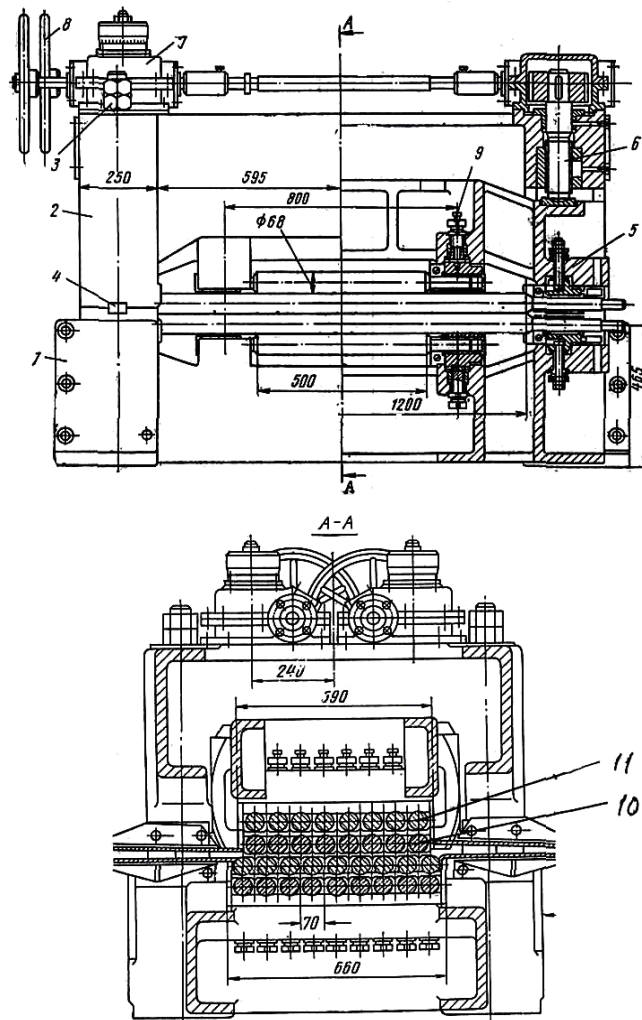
17 - роликова правильна машина з верхньою нахилу траверзою: 1, - станина нижня, 2 - станина верхня, 3 – болт, 4 - шпонка, 5 – траверза, 6 – натискний гвинт, 7 – натискний устрій, 8 – штурвал, 10 – робочий ролик, 11- опорний ролик.
